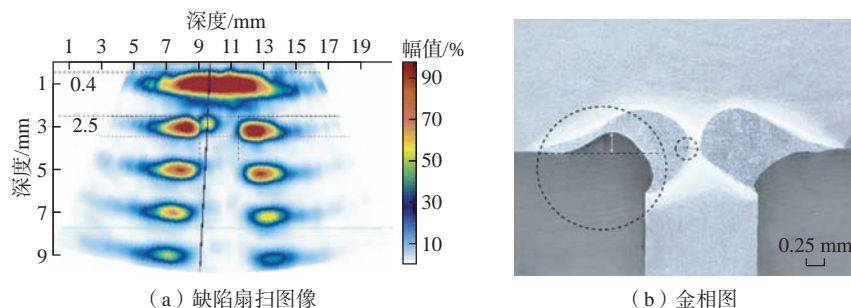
焊缝咬边缺陷的扇扫图和金相图(A₃ 试样)
